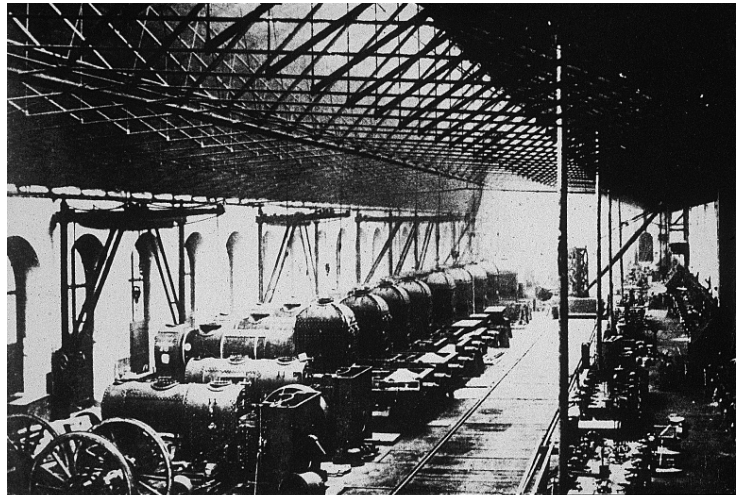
Borsig, Lokomotivwerkstatt an der Chausséestraße, Berlin, 1844, 1856
